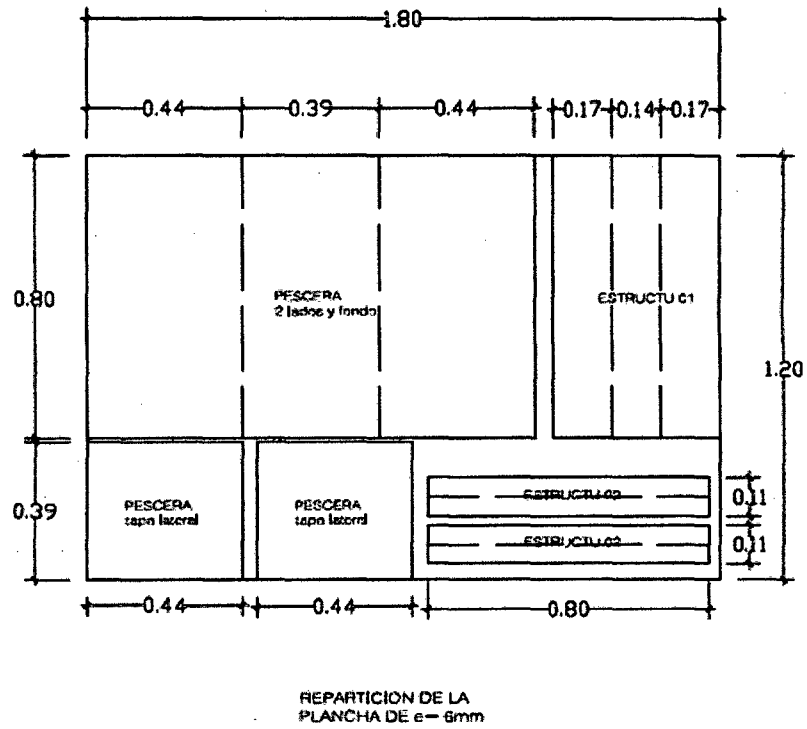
Distribución de las estructuras en la plancha de acrílico de 1.20mx1.80mx6mm.
